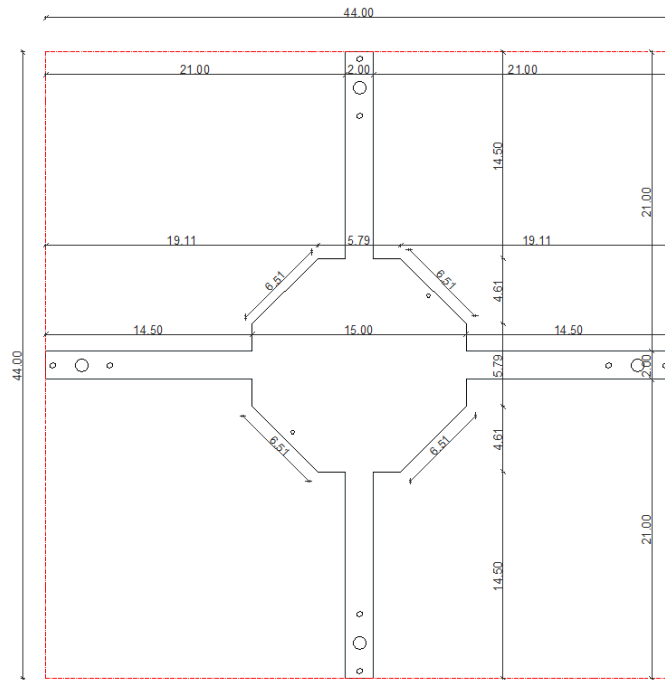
Plano de estructura. Medidas en centímetros de estructura del cuadricóptero.
